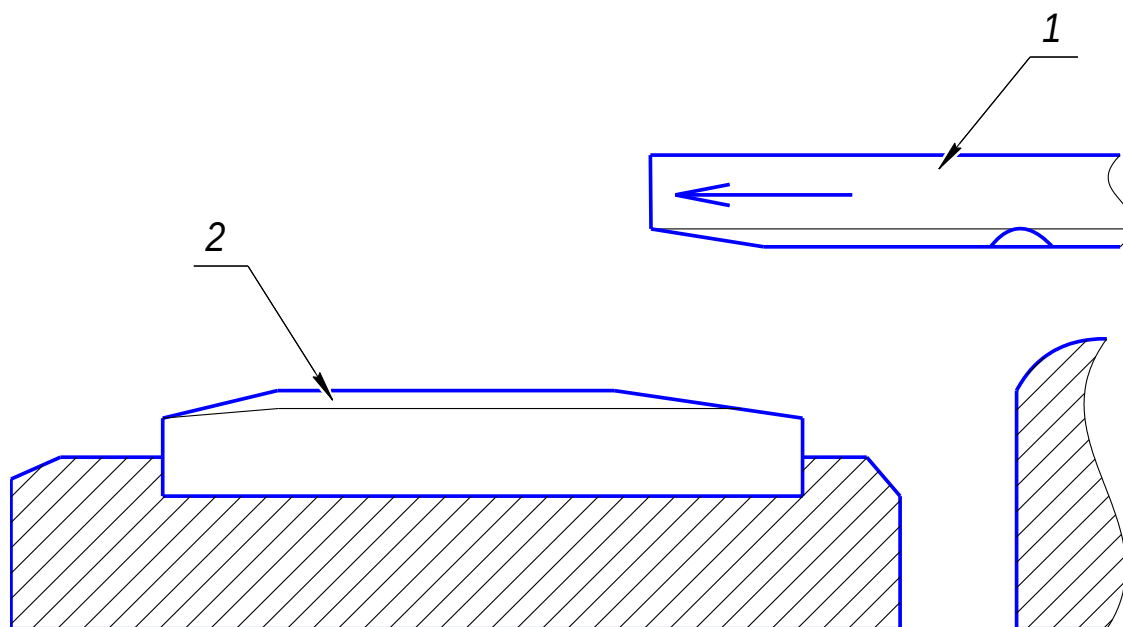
Накатывание специализированными плашками: 1 – подвижная плашка с несколькими заборными частями, 2 – неподвижная плашка
